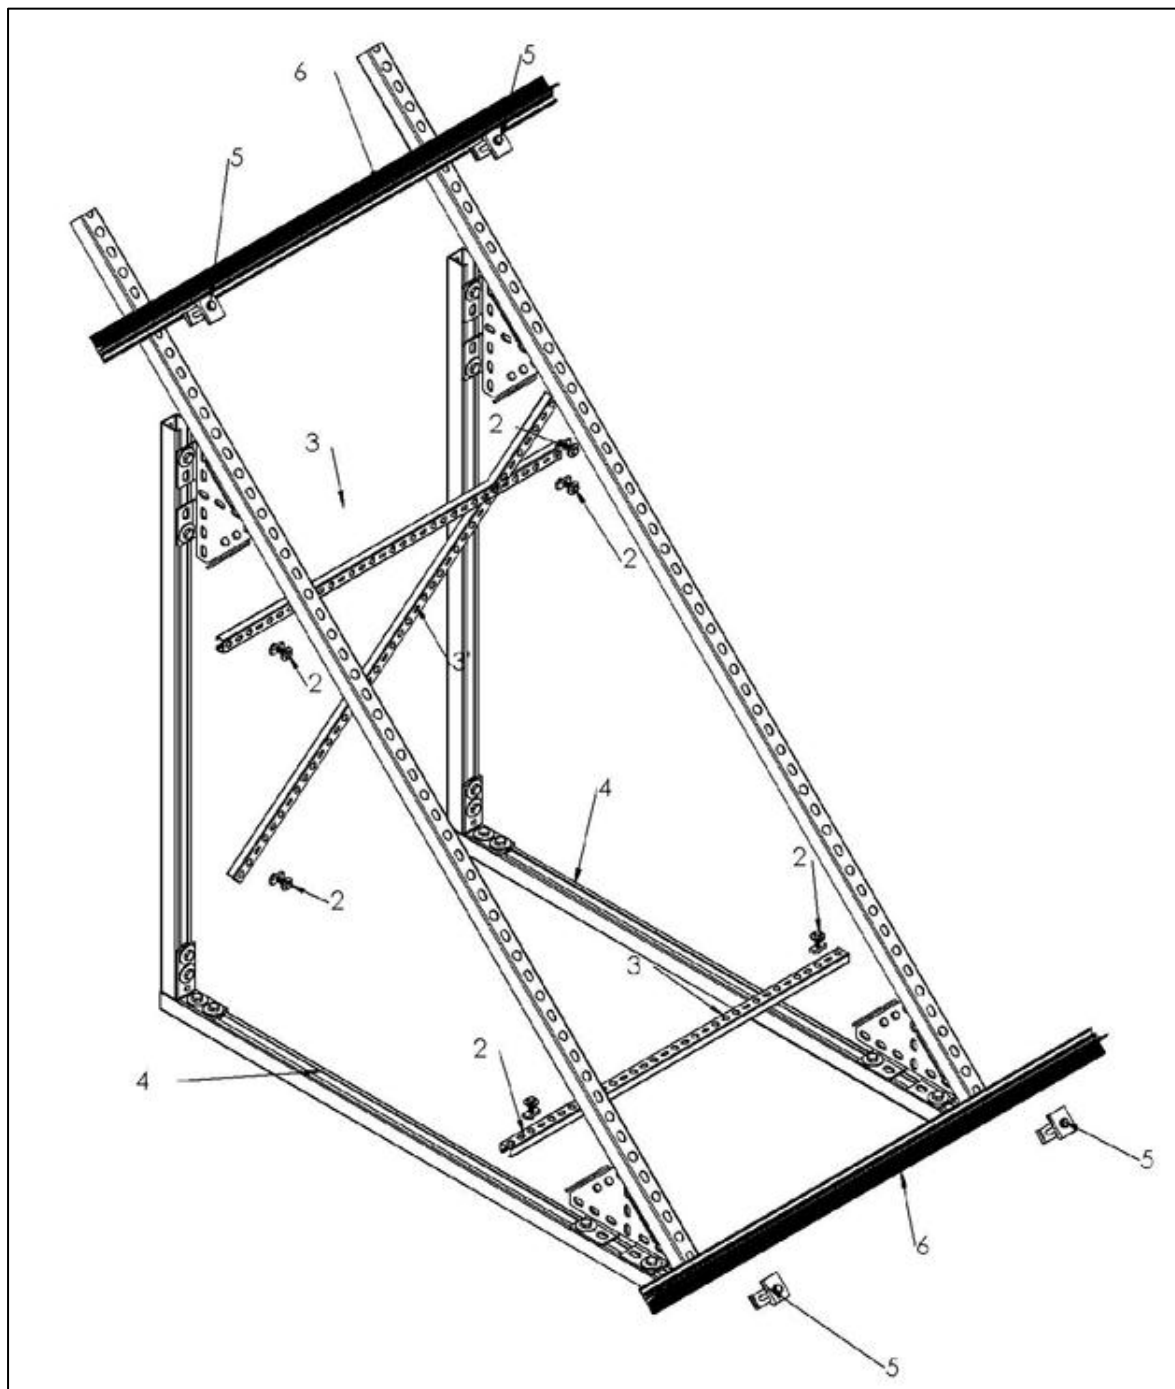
Vue éclatée et assemblée du châssis à 45°
